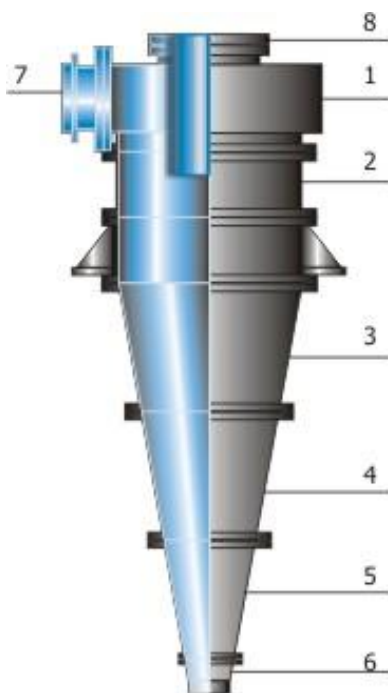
Конструкция гидроциклона: 1– камера приемная ; 2– цилиндр;
